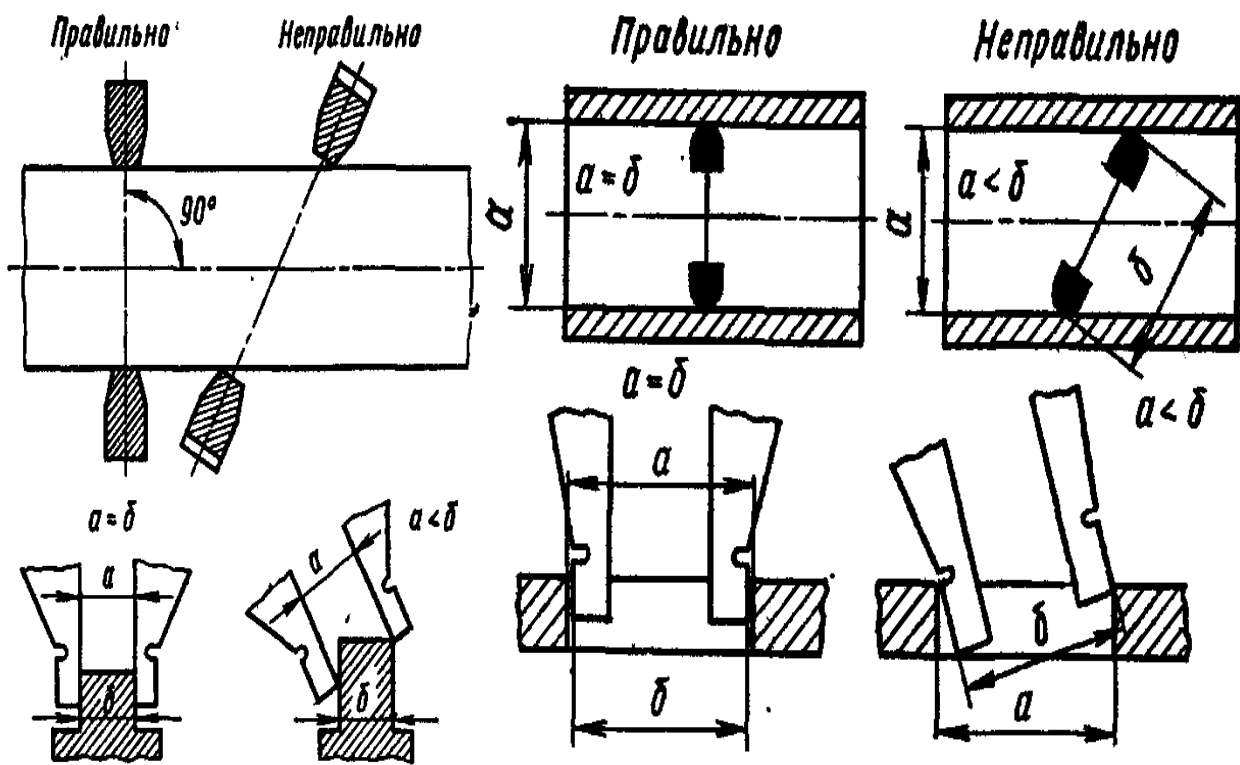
Установка штангенциркуля при измерении наружных поверхностей
